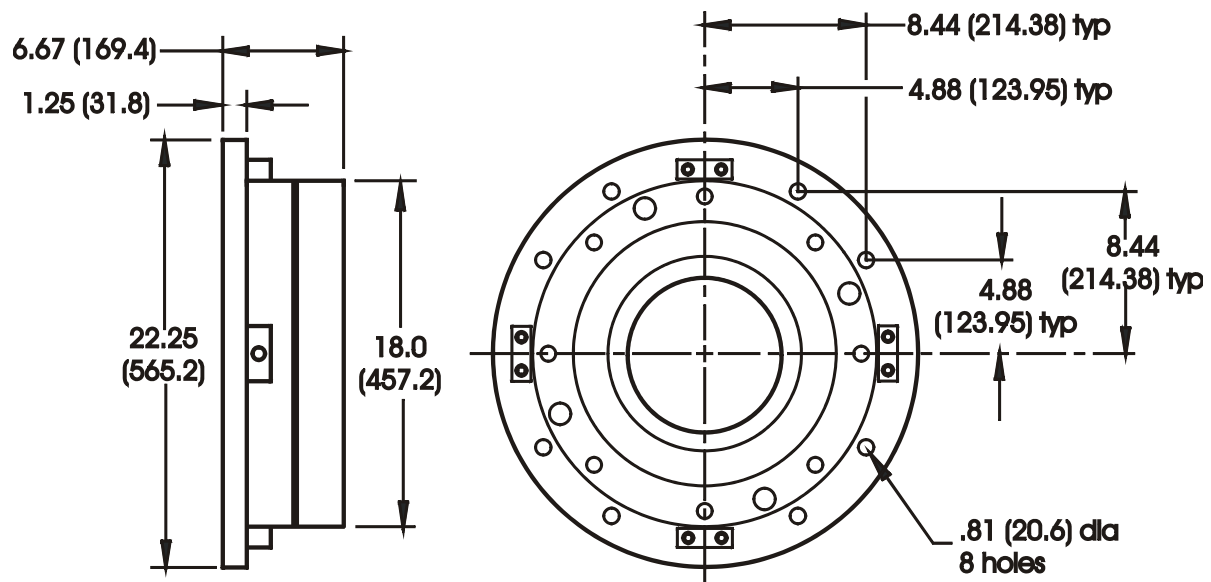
Dimensiones del conjunto de rodamientos autoalineador sin araña
